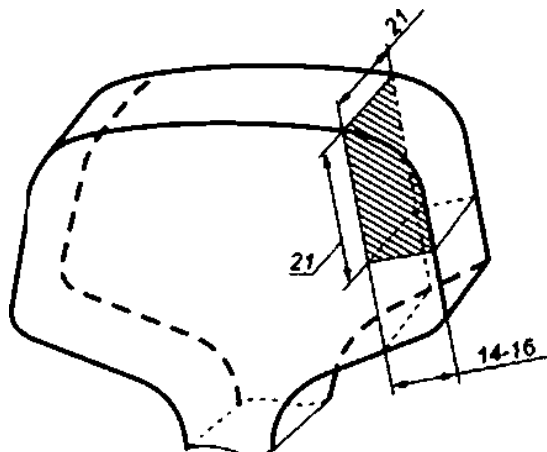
Схема расположения шлифа для контроля неметаллических включений
